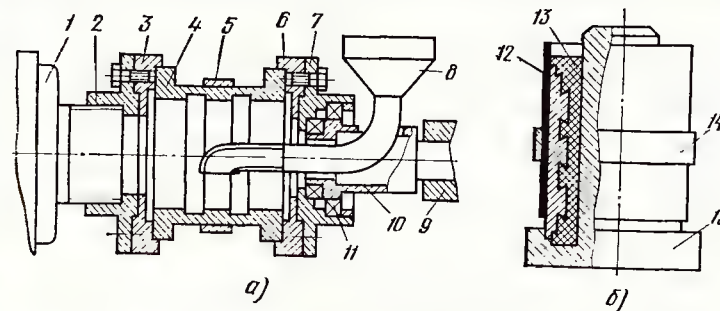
Приспособление для центробежной заливки (а) и форма для ручной заливки (б) вкладышей
